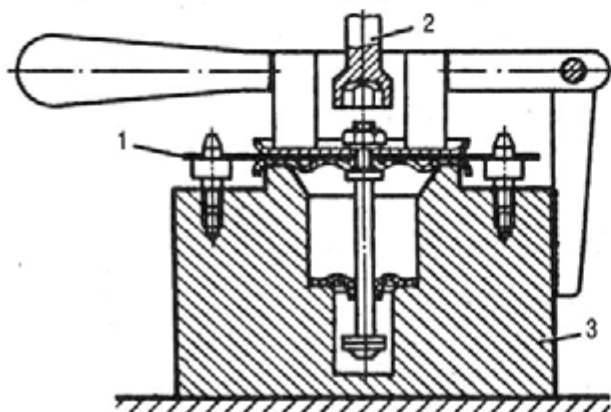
Приспособление для сборки диафрагмы: 1 - диафрагма; 2 - ключ; 3 - корпус приспособления
